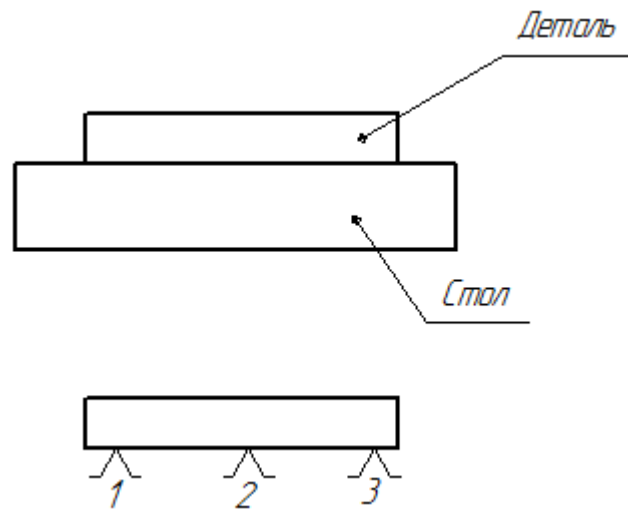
Схема базування заготовки на вакуумному столі [31]
